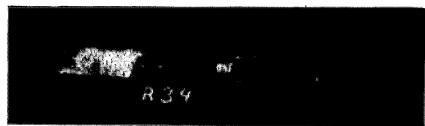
Röntgenbild (Positiv) einer schlechten Schweißung.
